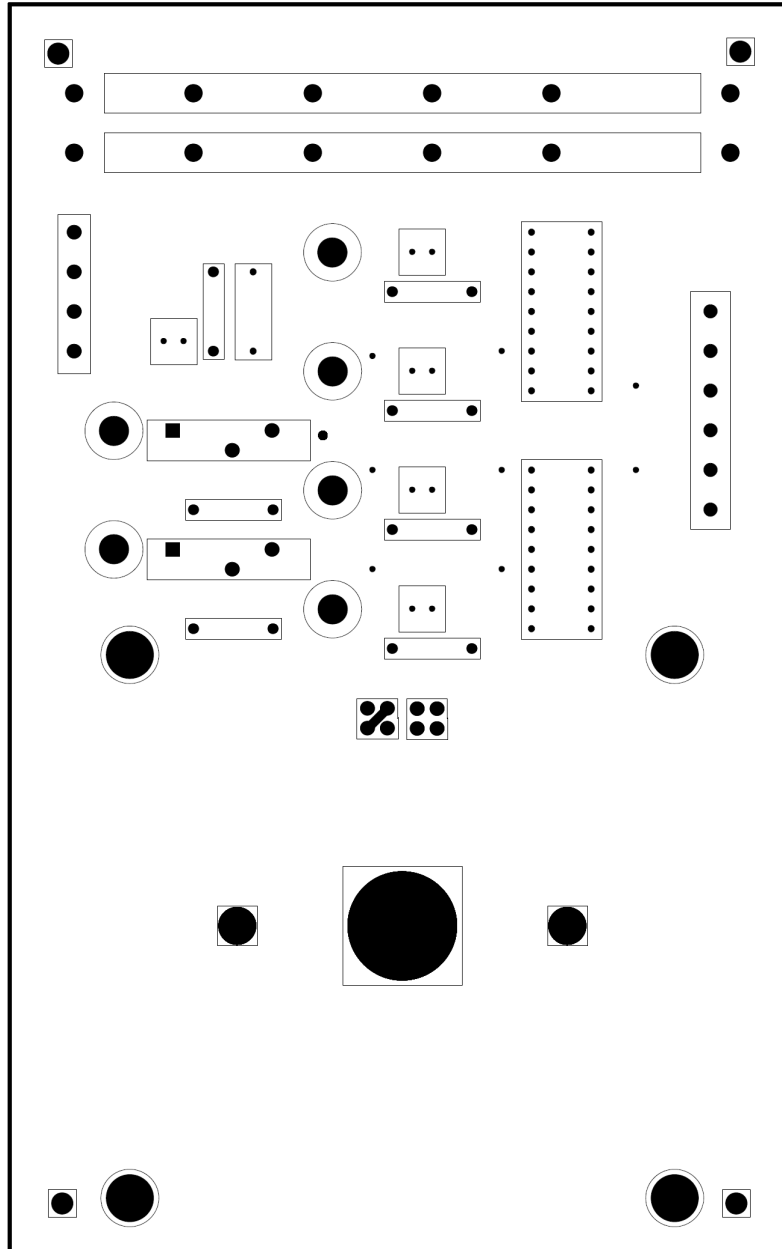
Capa de perforacions (DRL) de la PCB de la interfície per al motor unipolar
